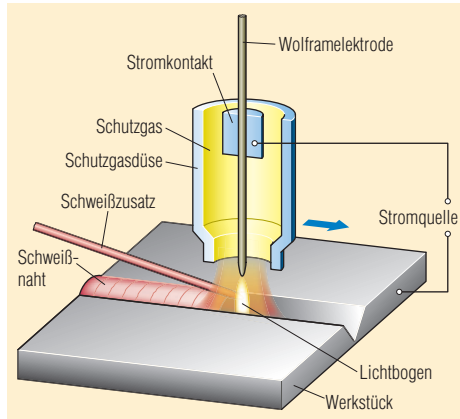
Prinzip des WIG-Schweißens.
